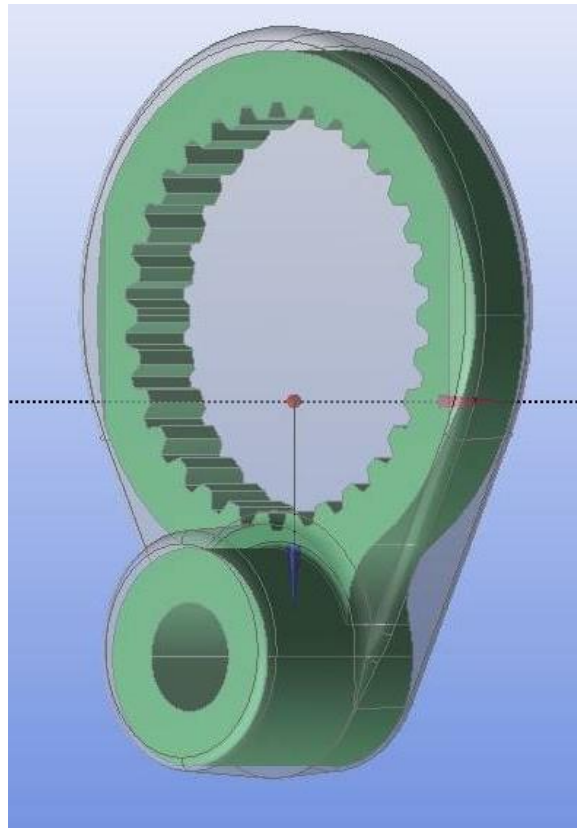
CAD-моделі заготовки та деталі після суміщення головних центральних осей інерції
